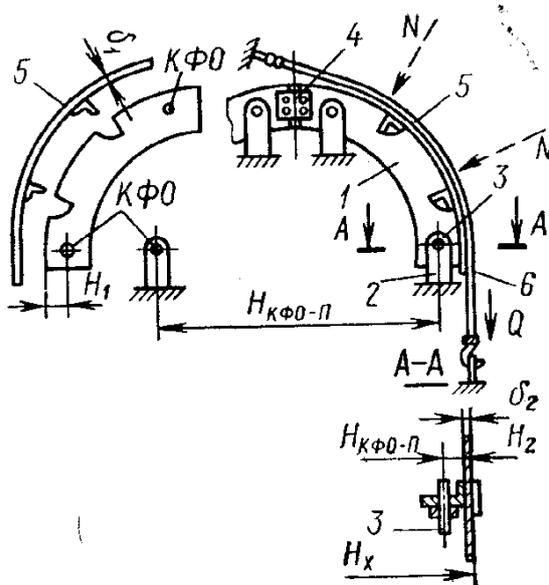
Базирование по КФО при установке элементов каркаса в сборочное положение: 1- шпангоут; 2- кронштейн сборочного приспособления; 3 – фиксатор; 4 – стык шпангоутов; 5 – прижим; 6 – натяжная лента;
